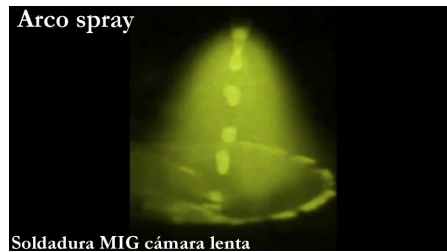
ARCO SPRAY SOLDADURA MIG(MAG CÁMARA LENTA.
